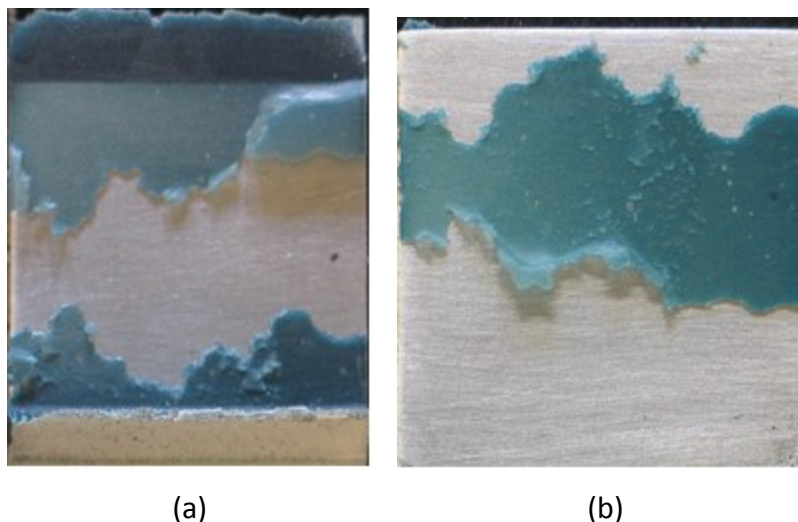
Provete 2 com “taper” em adesivo 45°. Superfície 1(a), Superfície 2 (b).
